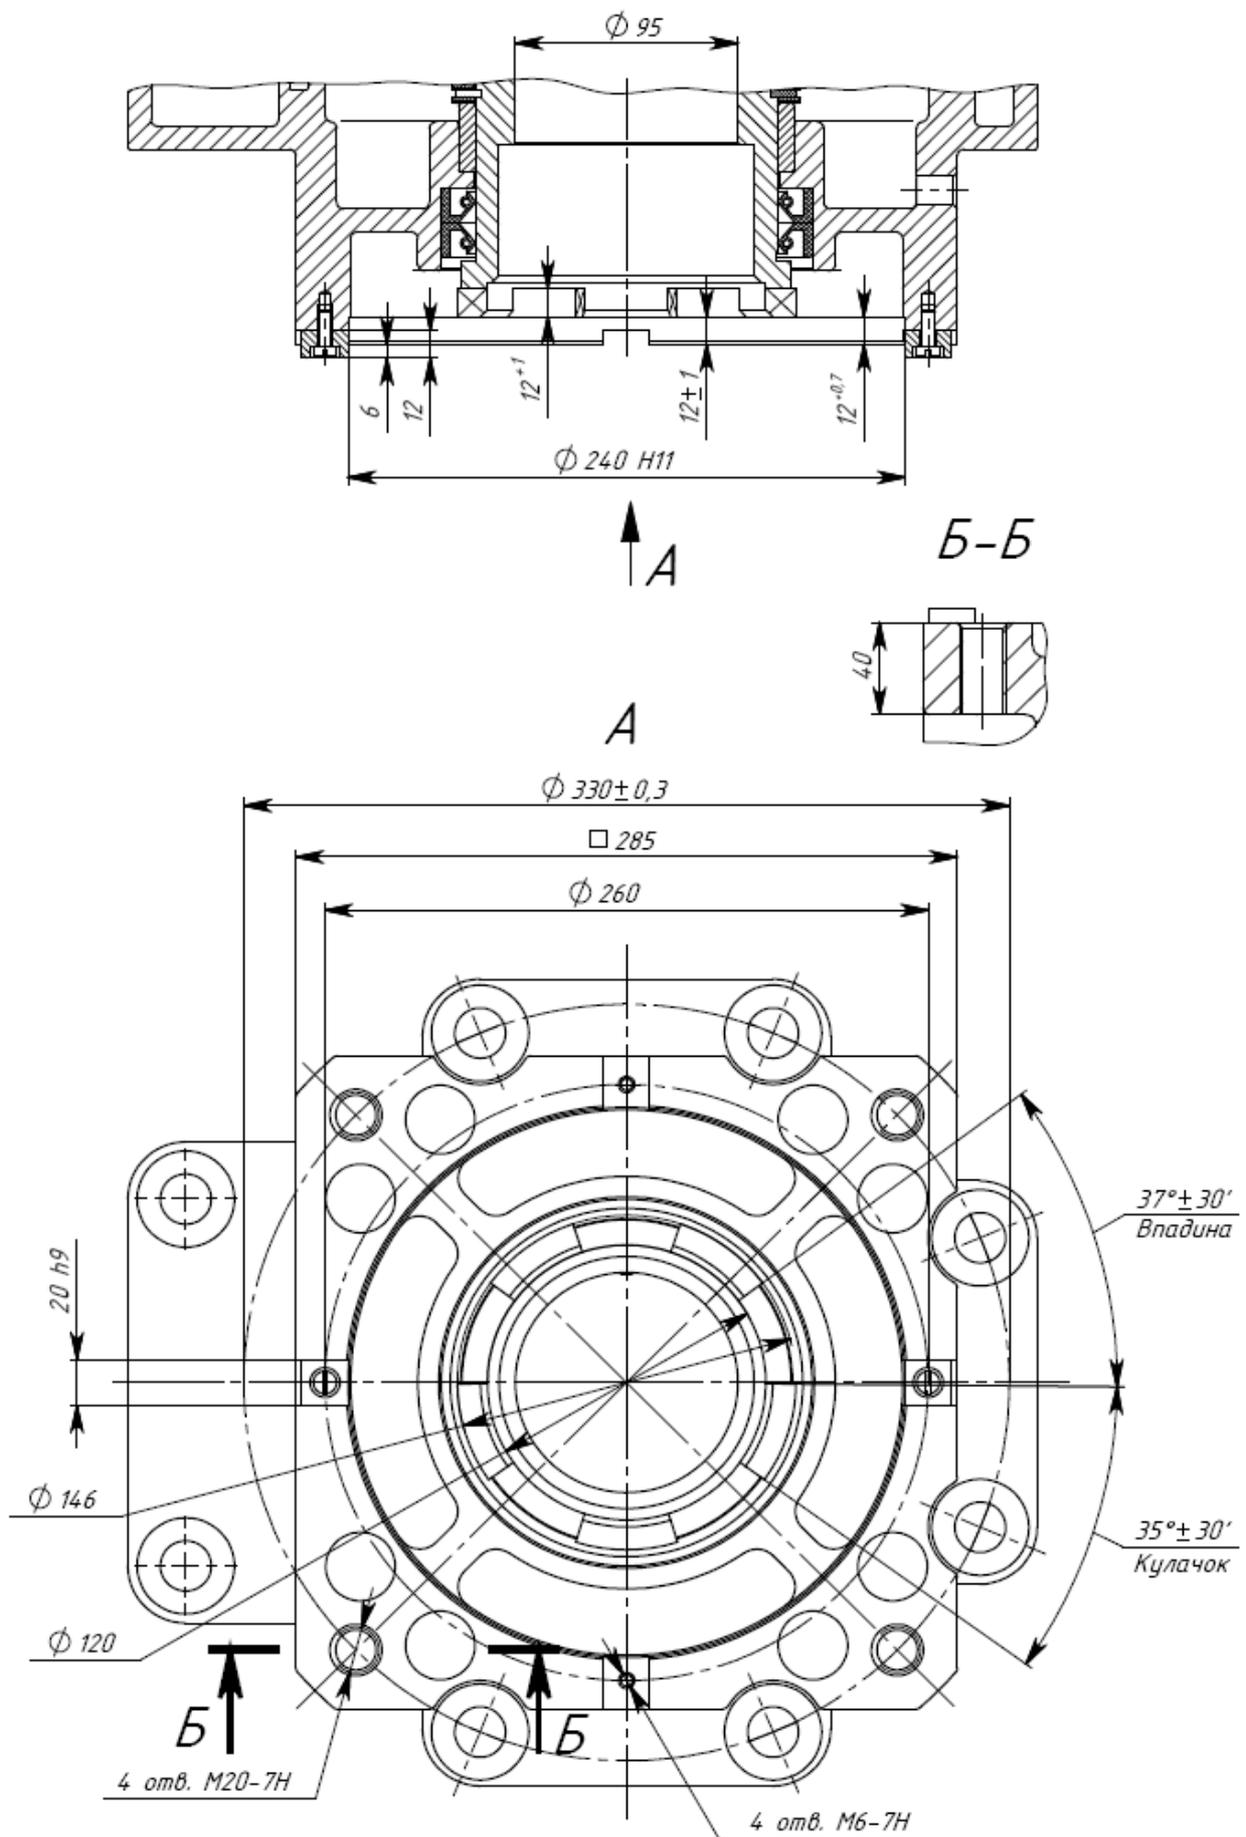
Присоединение типа Г для конструктивной схемы 43
